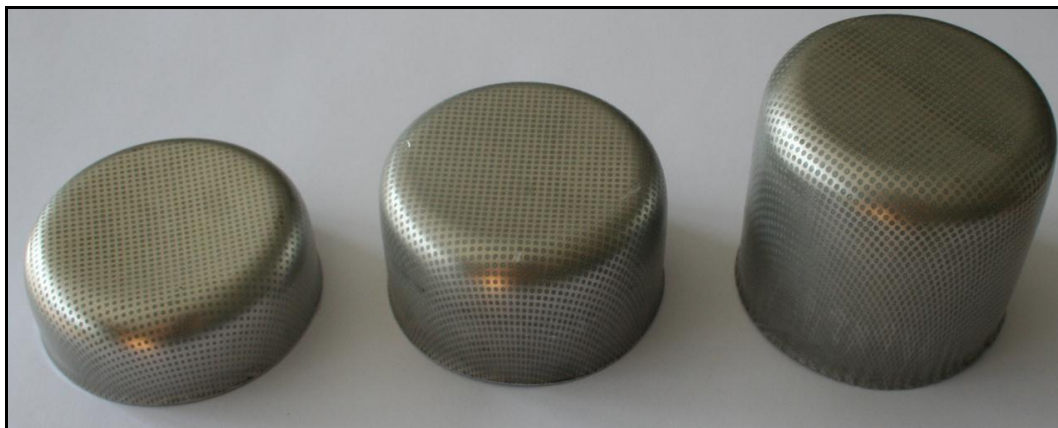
Připravený vzorek pro kalíškovou zkoušku
